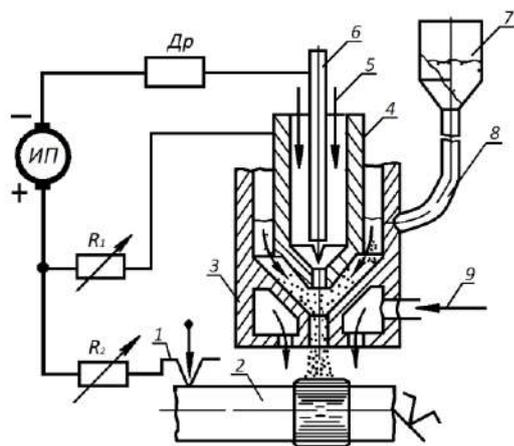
Схема процесса наплавки с вдуванием порошка в плазменную струю:
